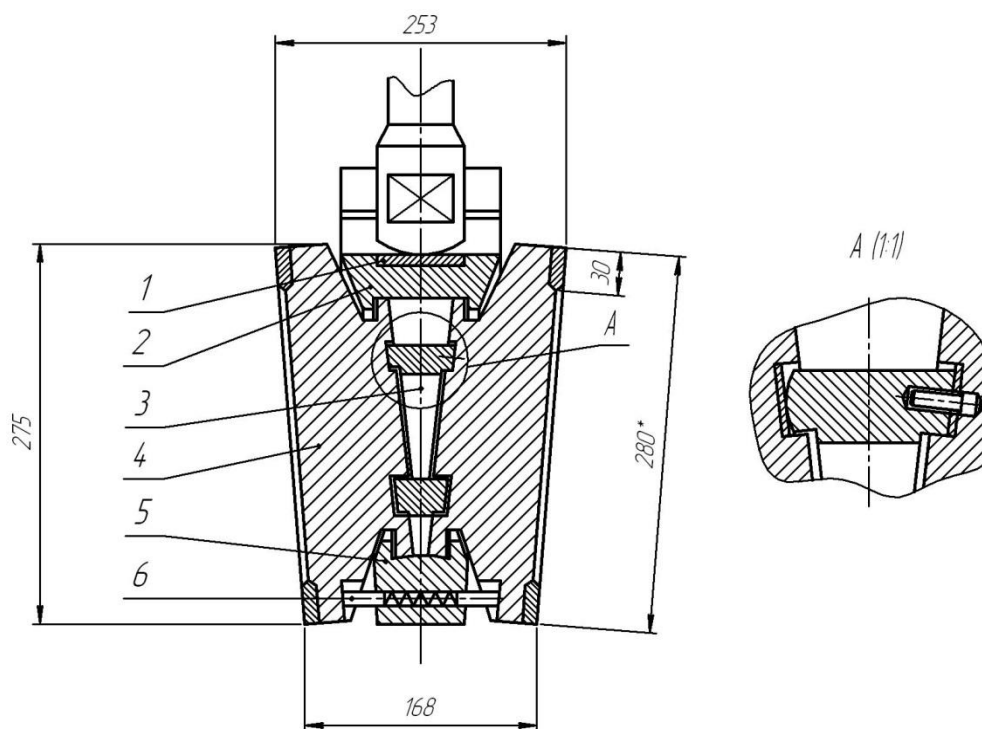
Схема прямооточной задвижки фонтанной арматуры
